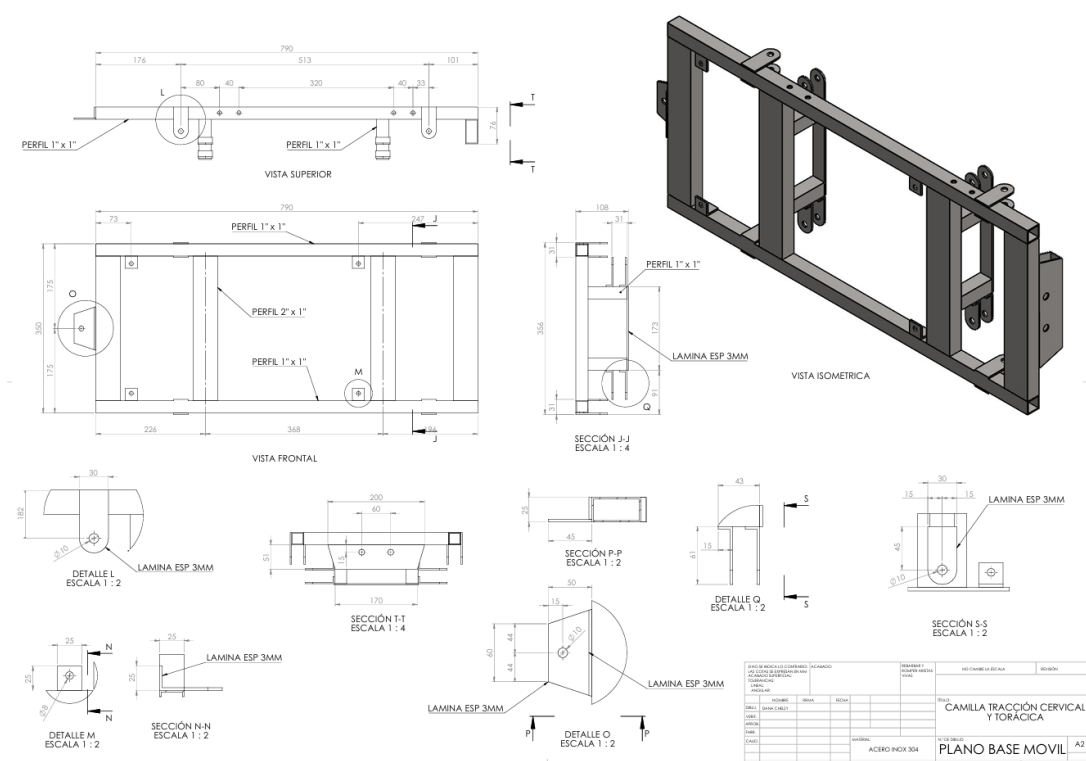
Plano de la estructura del carro móvil en el prototipo.
